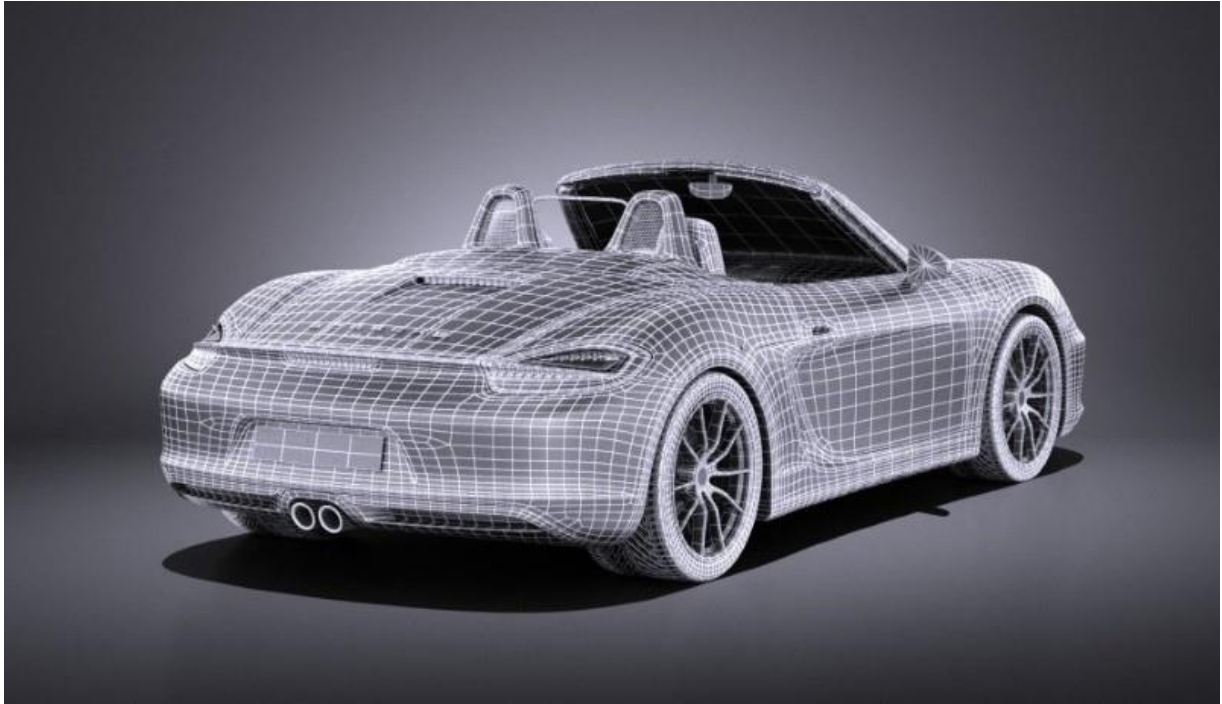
Трехмерная модель корпуса автомобиля
